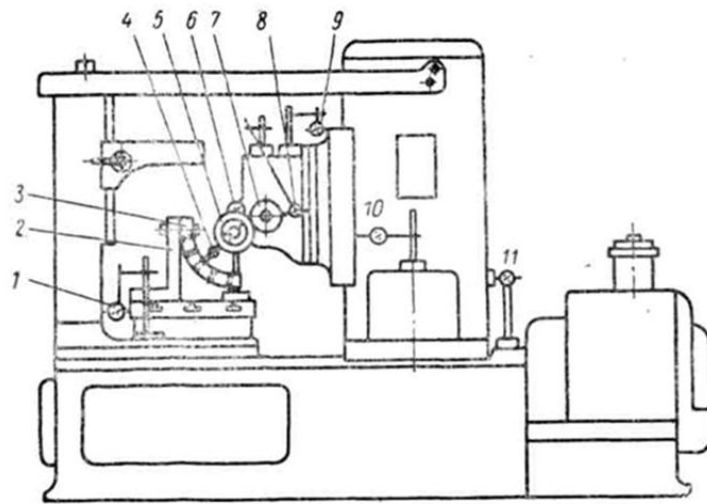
Установка вимірювання жорсткості зубофрезерного верстата
